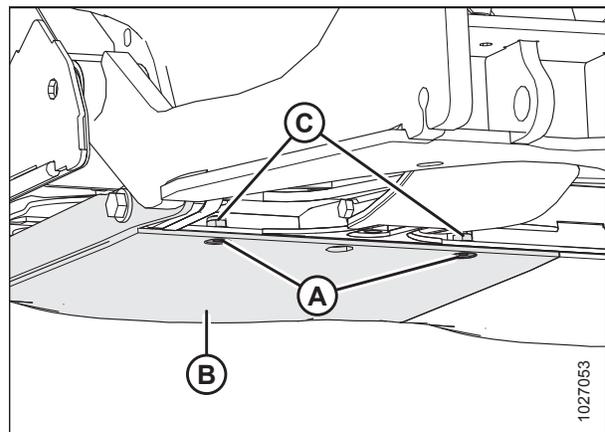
Jupe pare-pierres extérieure gauche – Vue arrière
